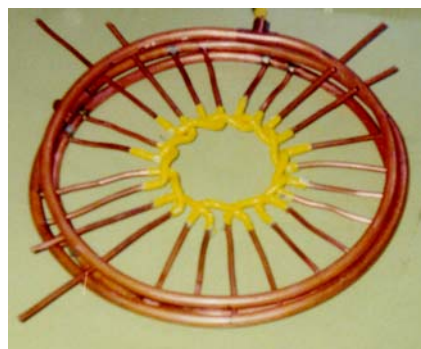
Semiéstator 1 a punto para la soldadura de las espiras.
